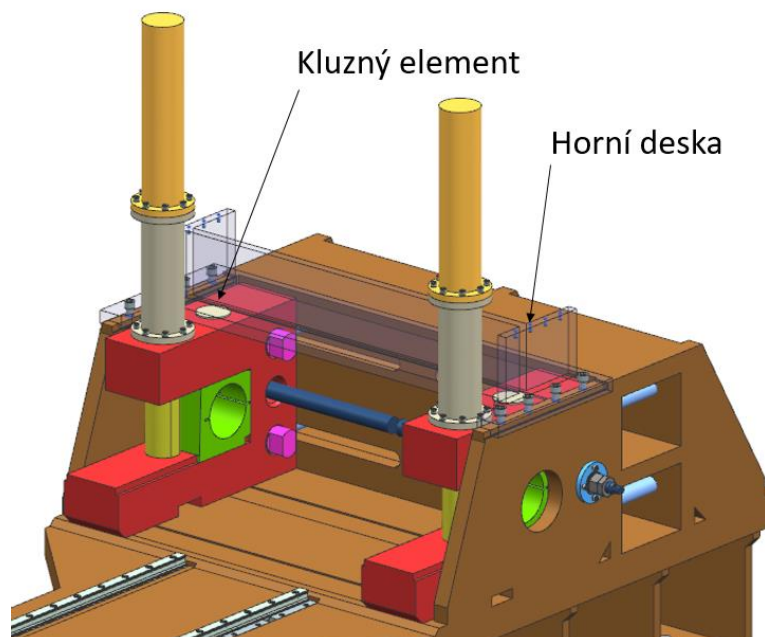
Upevnění testovaného HM – zasunutí objímek do konzol
